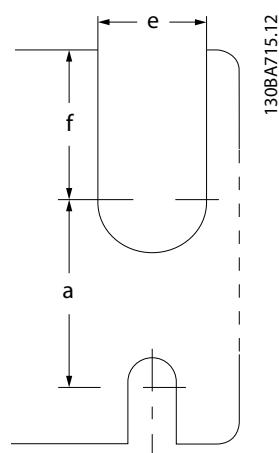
Pravilno montiranje sa zadnjom pločom
